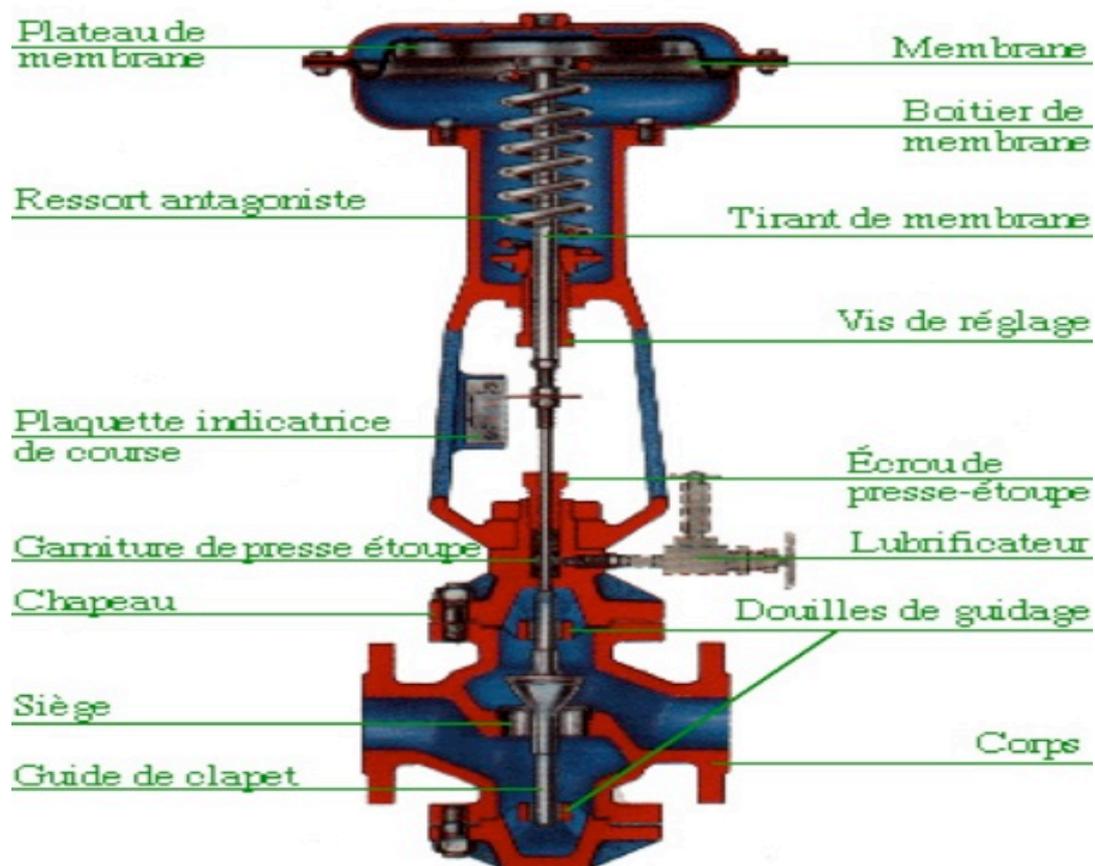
Vue en coupe d'une vanne de régulation pneumatique
